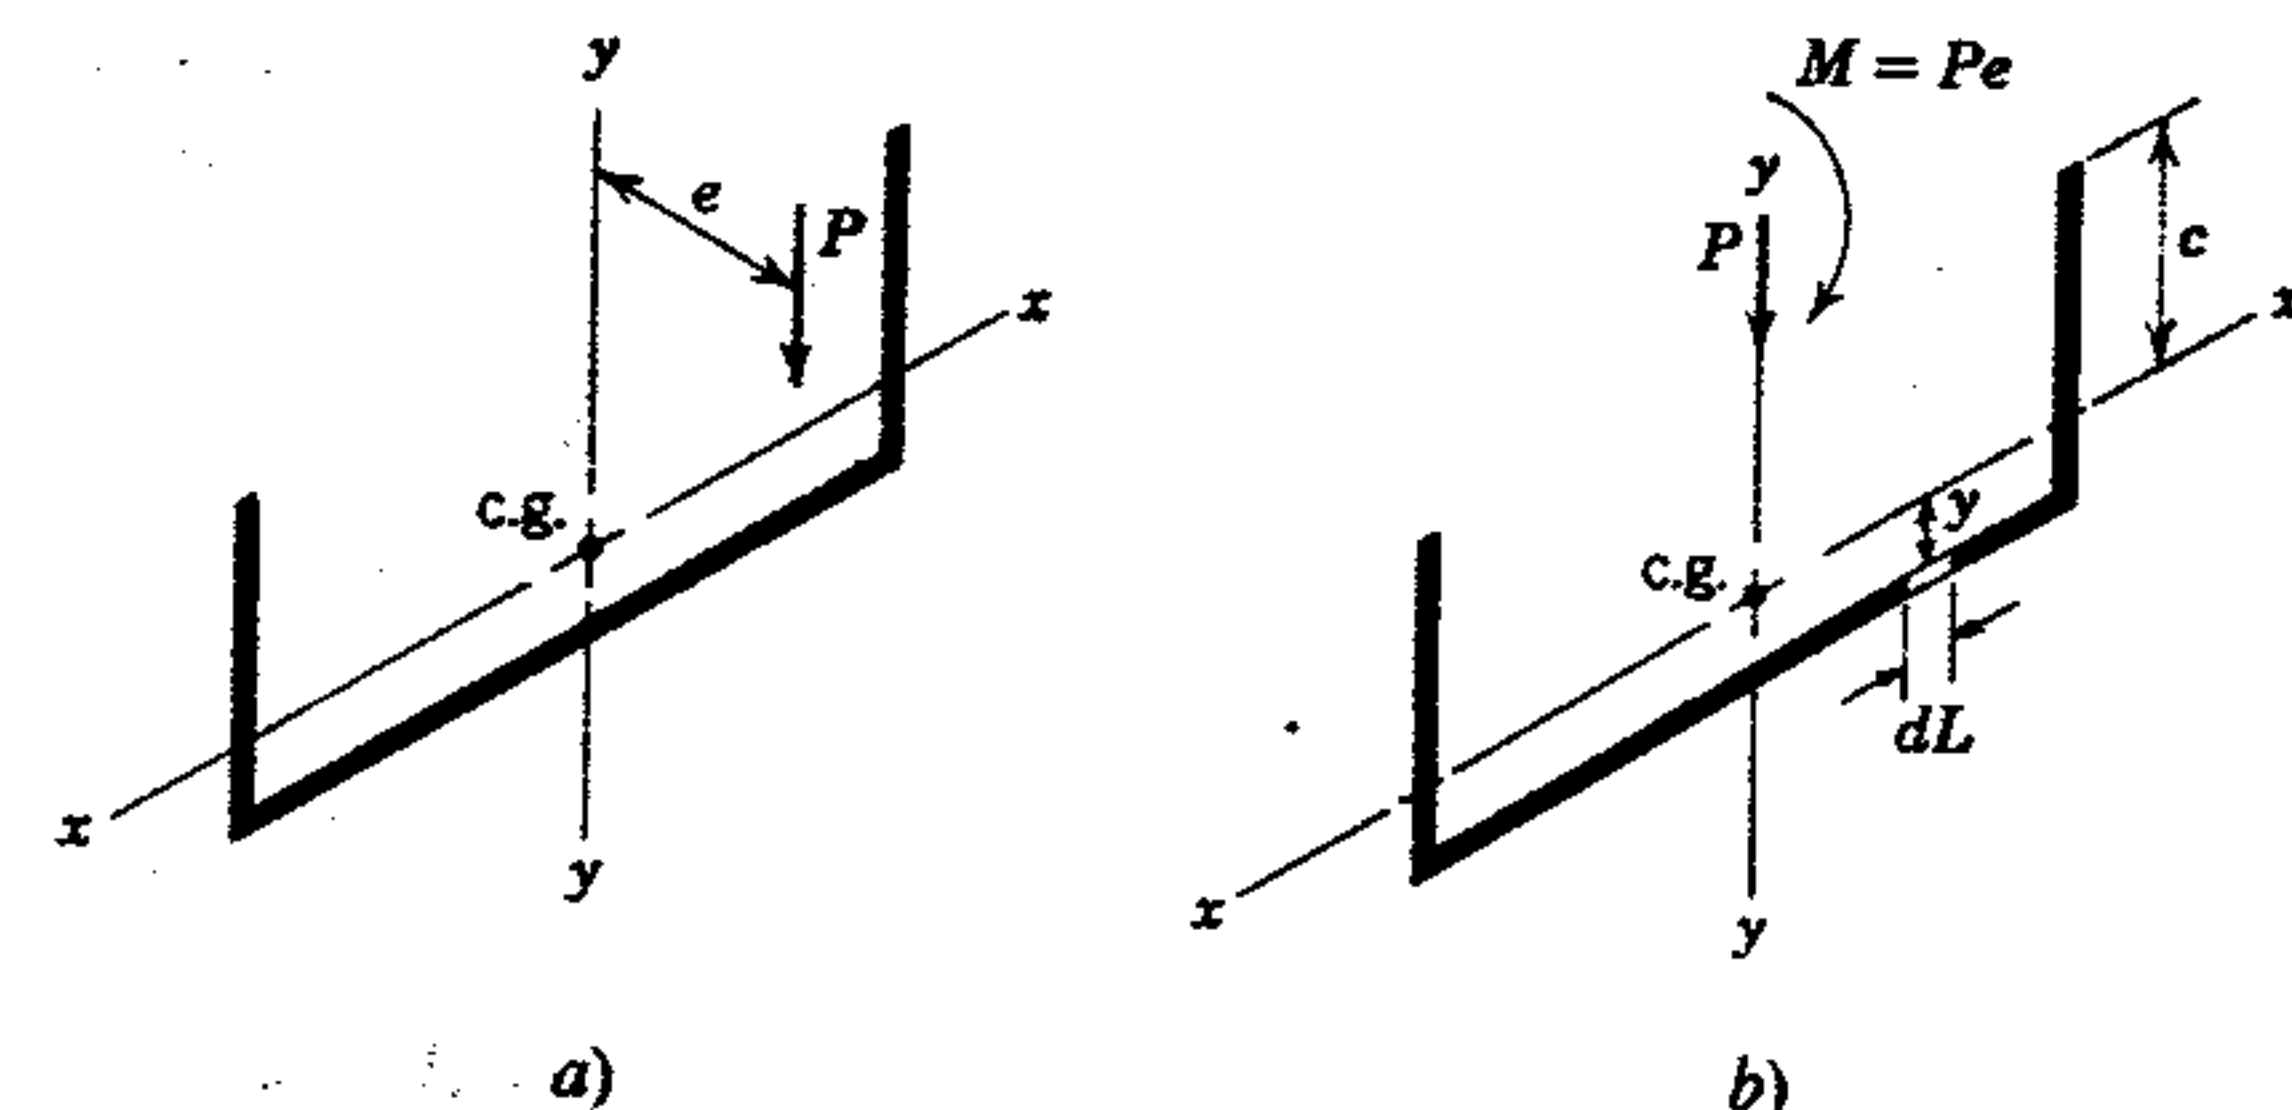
Excentricidad fuera del plano de las soldaduras.
